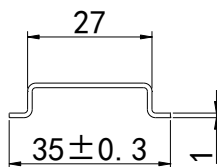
Габаритные размеры DIN-рейки для установки коммутатора PMP-6EC
